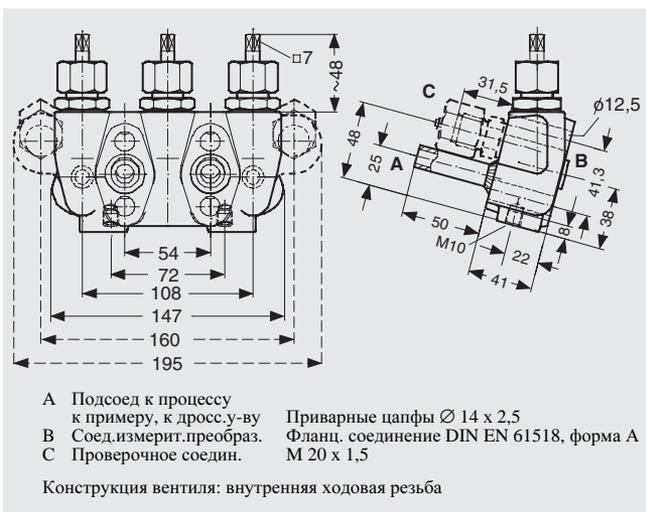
/93 Трехходовой вентильный блок DN 8 с приварной цапфой, размеры в мм
